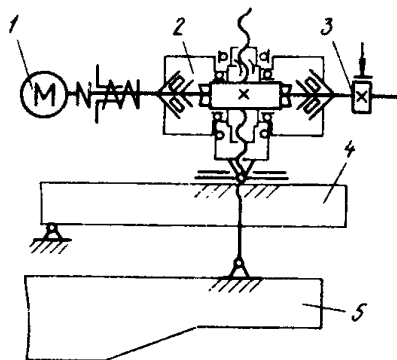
Кинематическая схема механизма подъема и опускания стрелы: Р.П. — рама противовеса; П.П. — платформа поворотная
